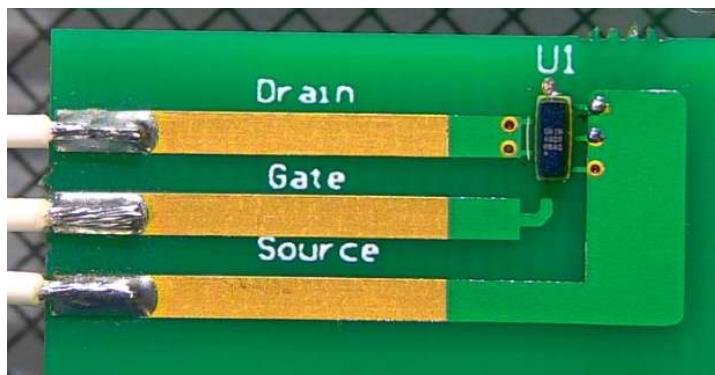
Puce RÉFÉRENCE_1 soudée sur le PCB (côté puce)
